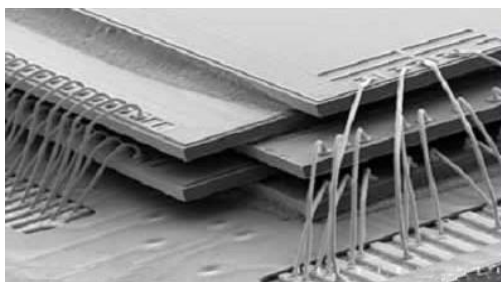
Фотография примера разварки выводов и системы в корпусе
